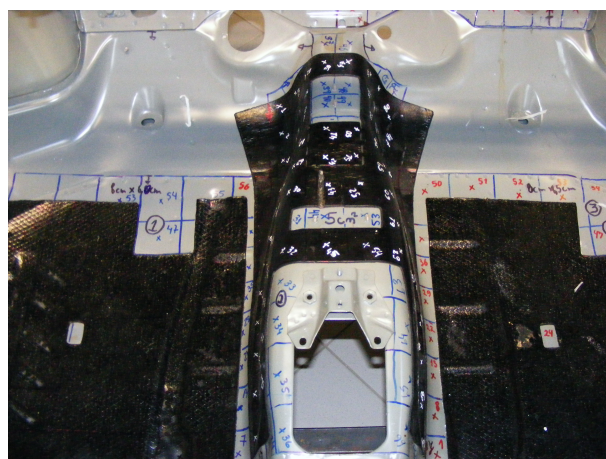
Detalhe do design da manta asfáltica aplicada.
